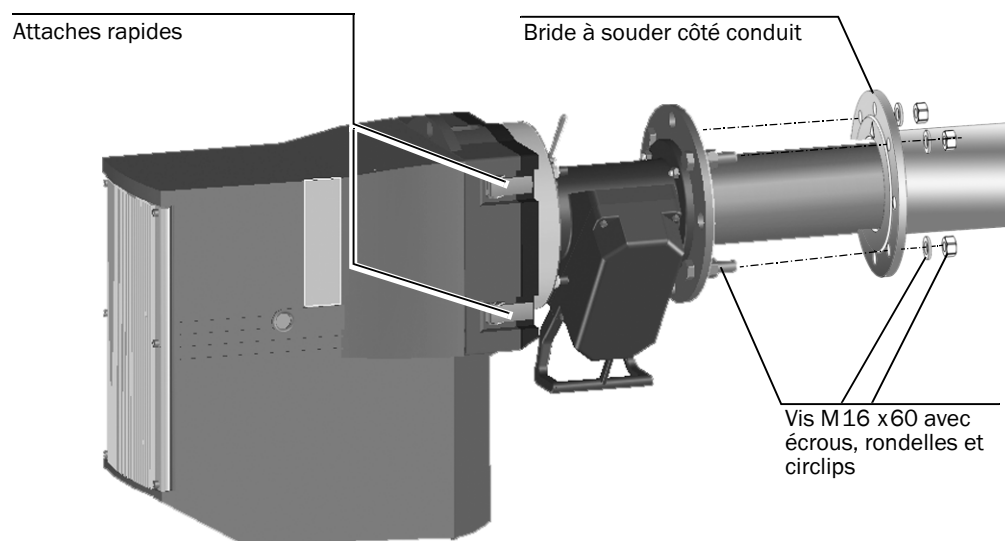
Montage de l'E/R avec la sonde de mesure sur la bride du conduit
